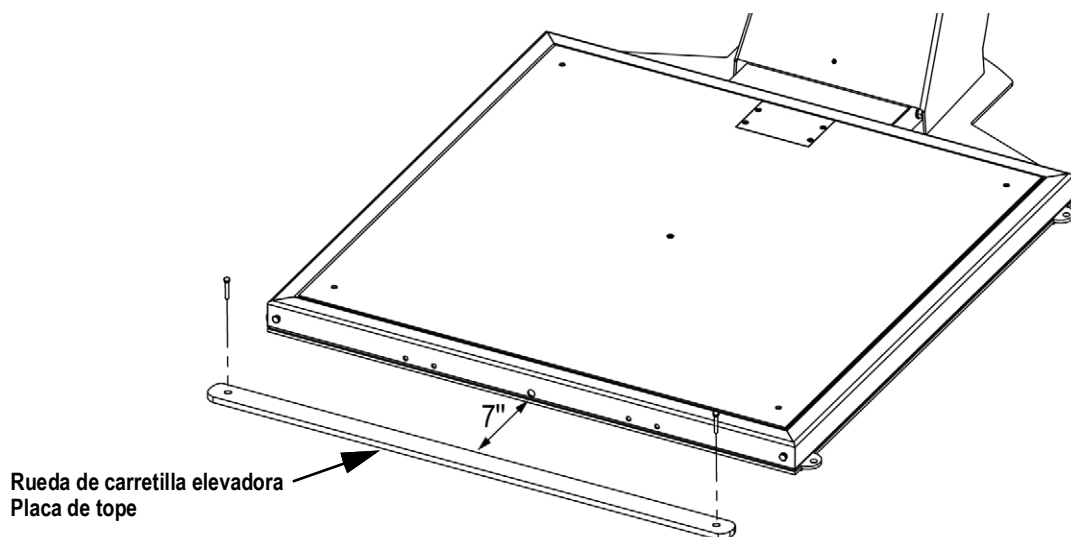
Placa de tope para ruedas de carretilla elevadora
